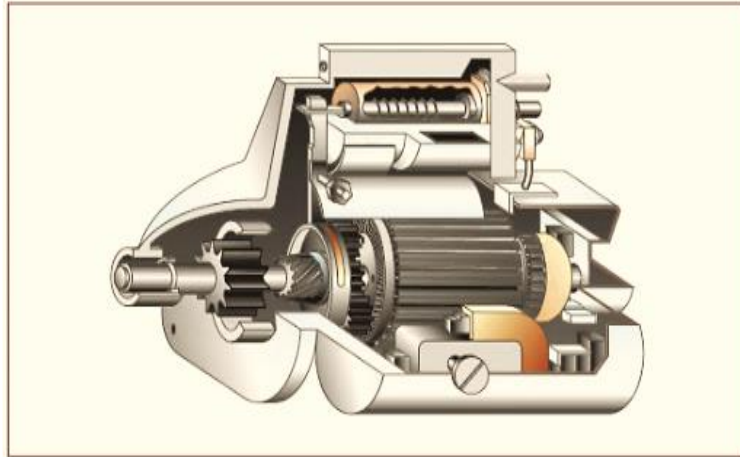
Motor de arranque por relé, horquilla y reductora
